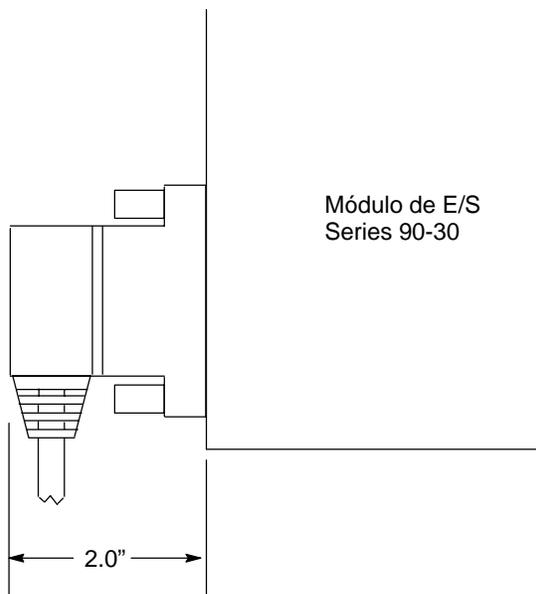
Dimensiones de profundidad del conector para los cables IC693CBL327/328
